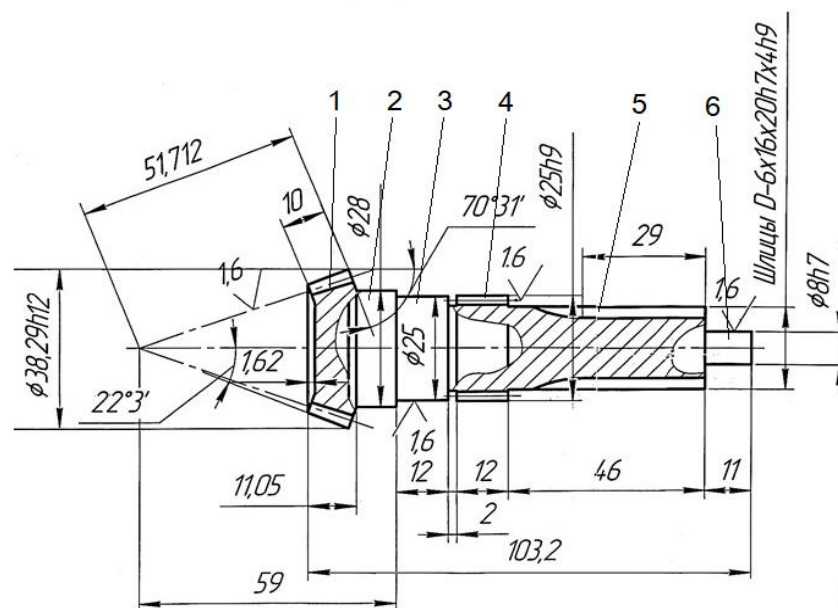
Конструкция вала-шестерни ударного механизма
